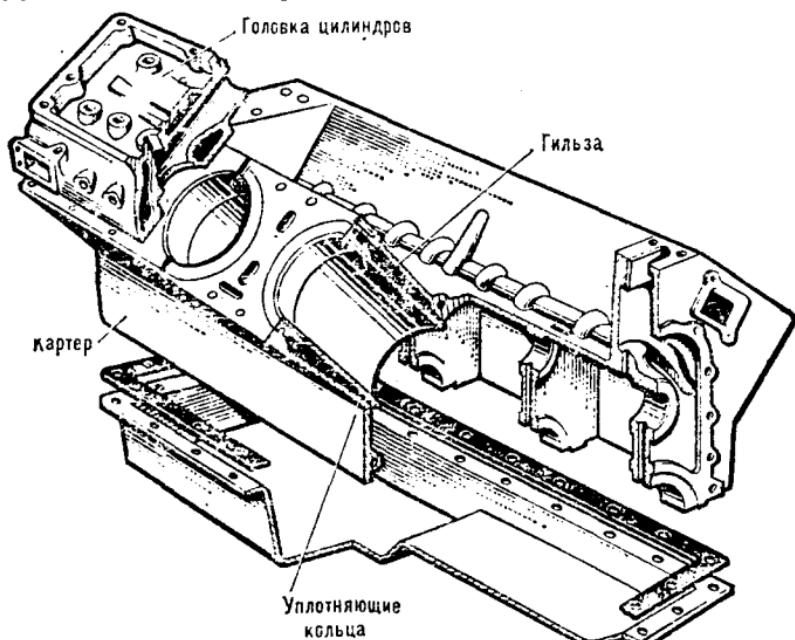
Блок цилиндров и головка цилиндров двигателя ЗИЛ-130
